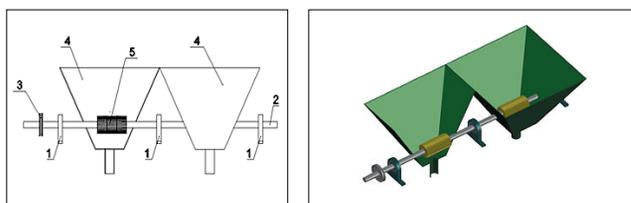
Схематический вид агрегата для внесения минеральных удобрений: 1 – хомуты для закрепления вала; 2 – вал измельчителя; 3 – шкив; 4 – бункеры; 5 – измельчитель
